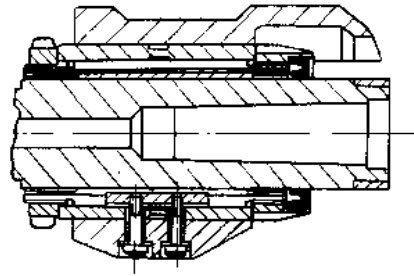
Y38 滚齿机刀架内圆外锥式轴承装配图
